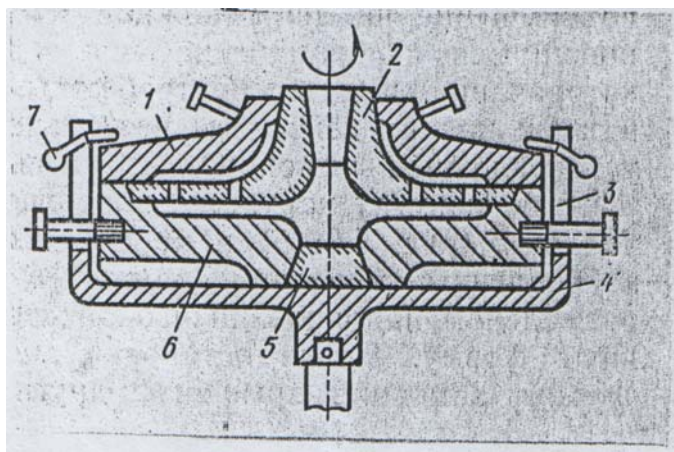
Металлическая форма с песчаным стержнем для получения фасонных отливок. 1- верхняя полуформа, 2- песчаный стержень, 3- прорези, 4- планшайба, 5- песчаная вставка, 6- нижняя полуформа, 7- центробежный зажим.
